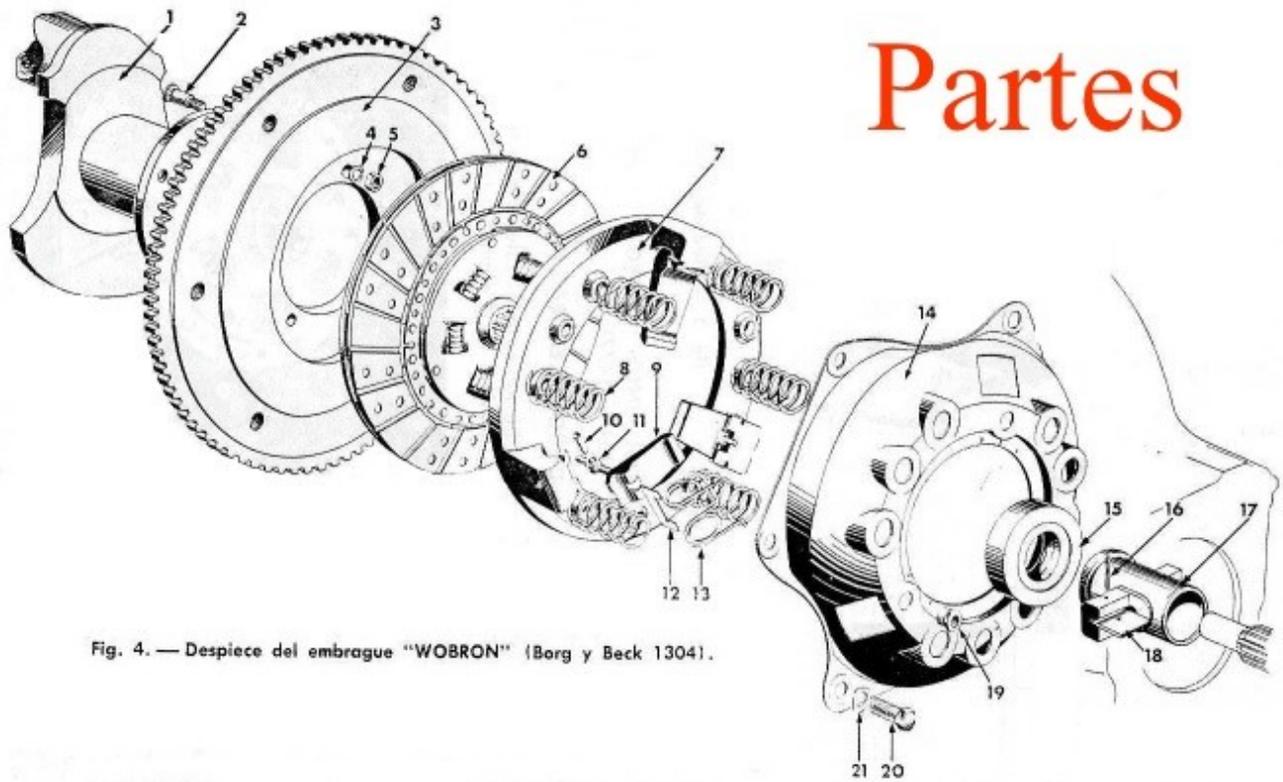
Despiece del embrague "WOBRON" (Borg y Beck 1304).
